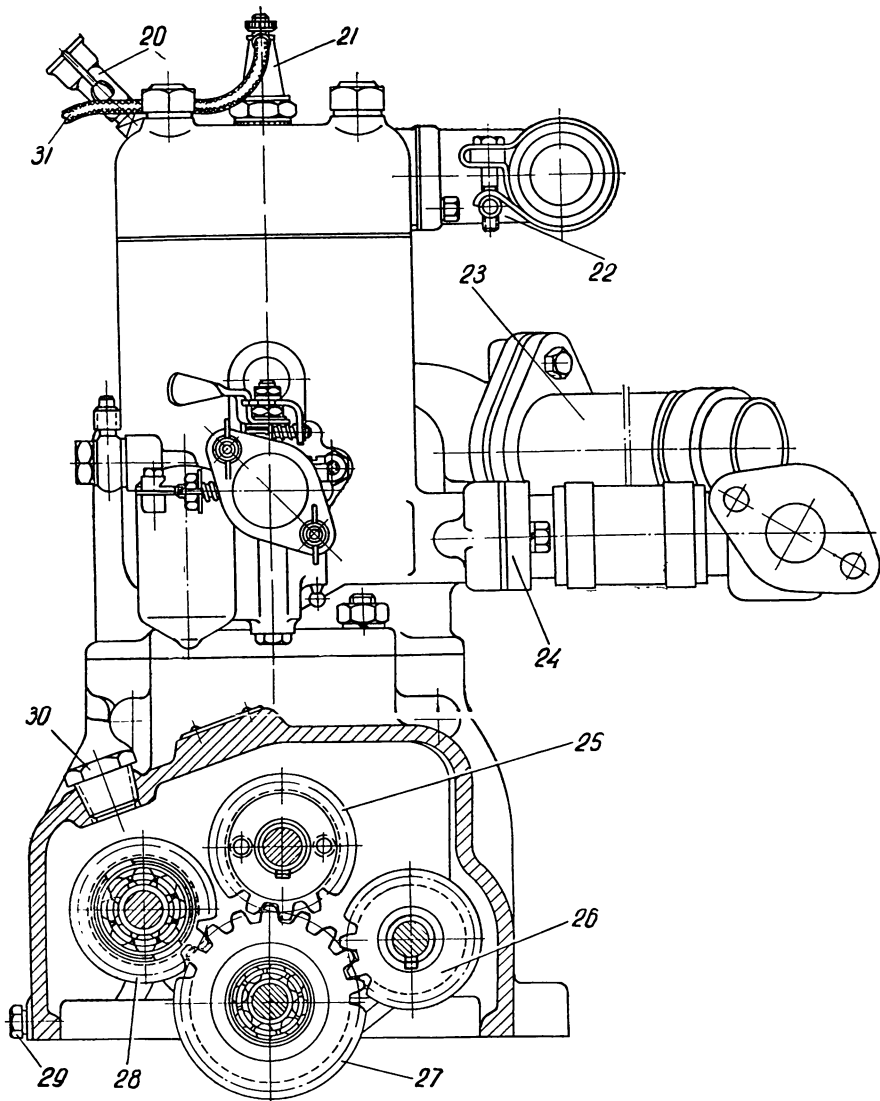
Пусковой двигатель ПД-10М (вид спереди с разрезом по шестерням распределения):
